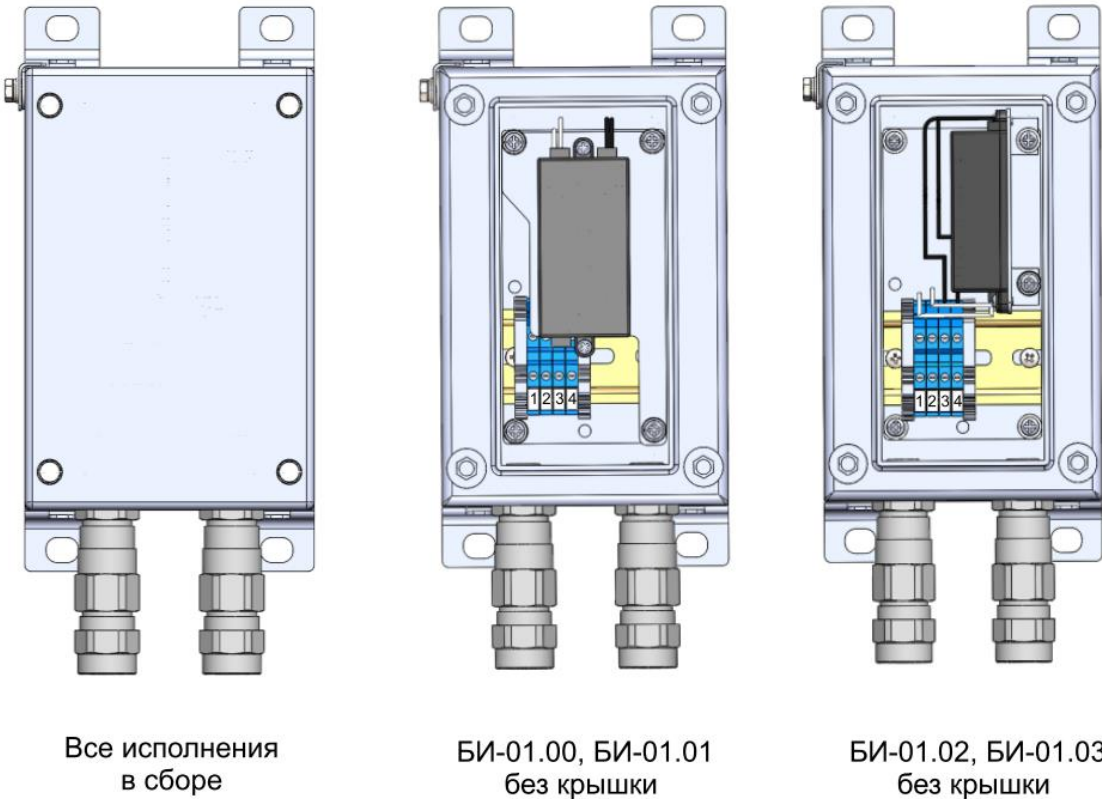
Блок исполнительный БИ-01. Внешний вид
